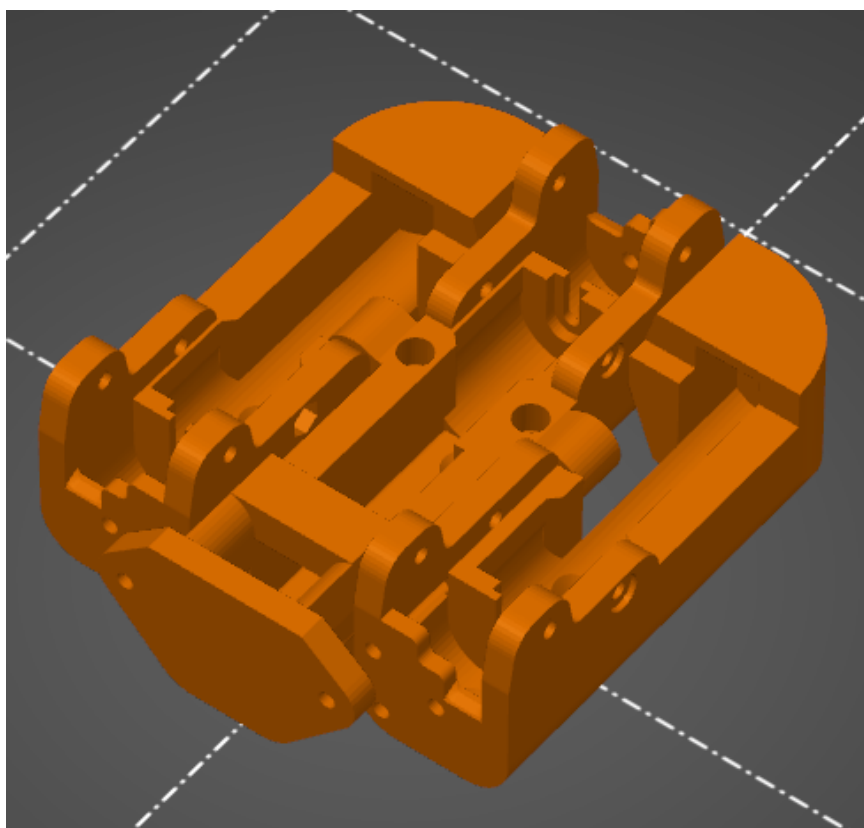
Sestavené prsty pro robotické chapadlo
